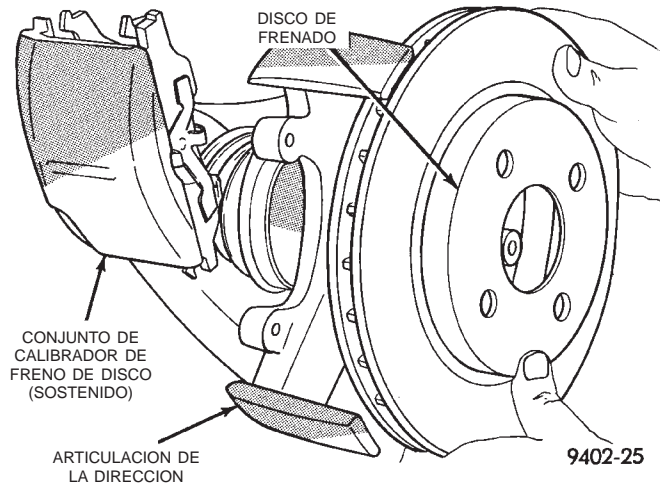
Desmontaje del conjunto del calibrador de freno e instalación
